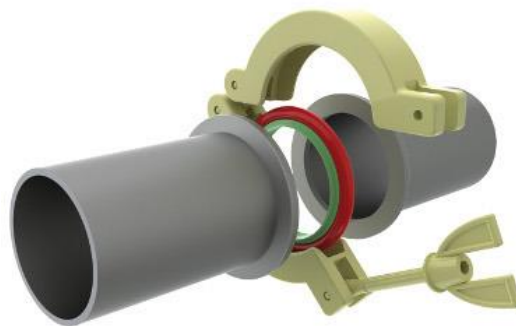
Ensamblaje de una conexión ISO KF (Fuente: The Vacuum Projects)
